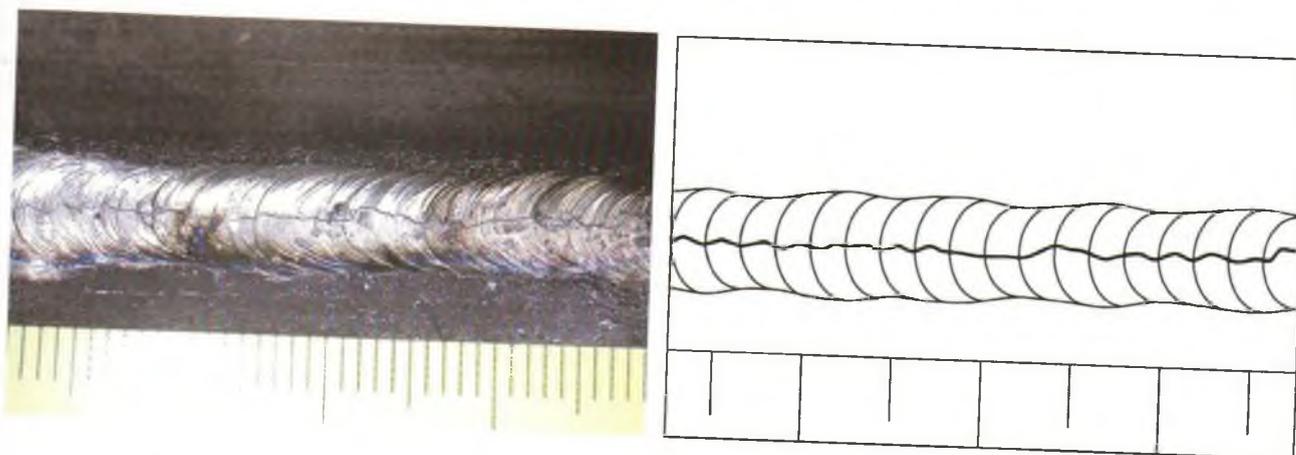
Продольная трещина нахлесточного сварного соединения строительной конструкции
